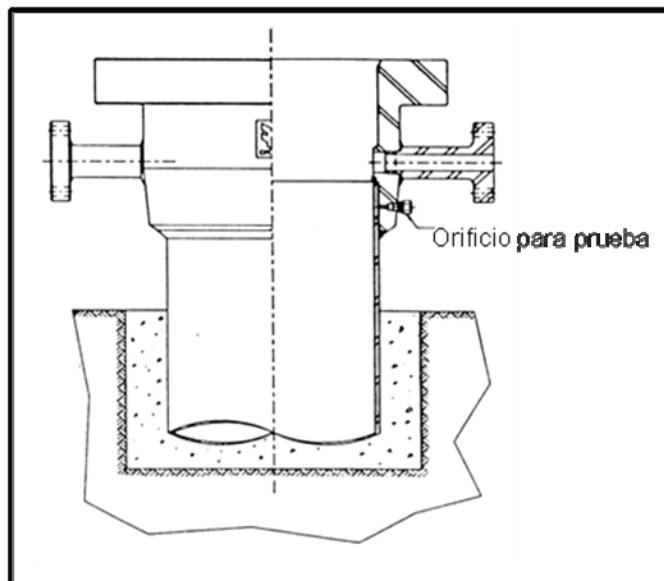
CABEZAL DEL TR SOLDABLE MARCA FIP
